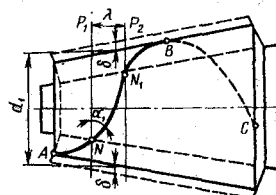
Схема расположения витка пряжи на поверхности конической бобины
